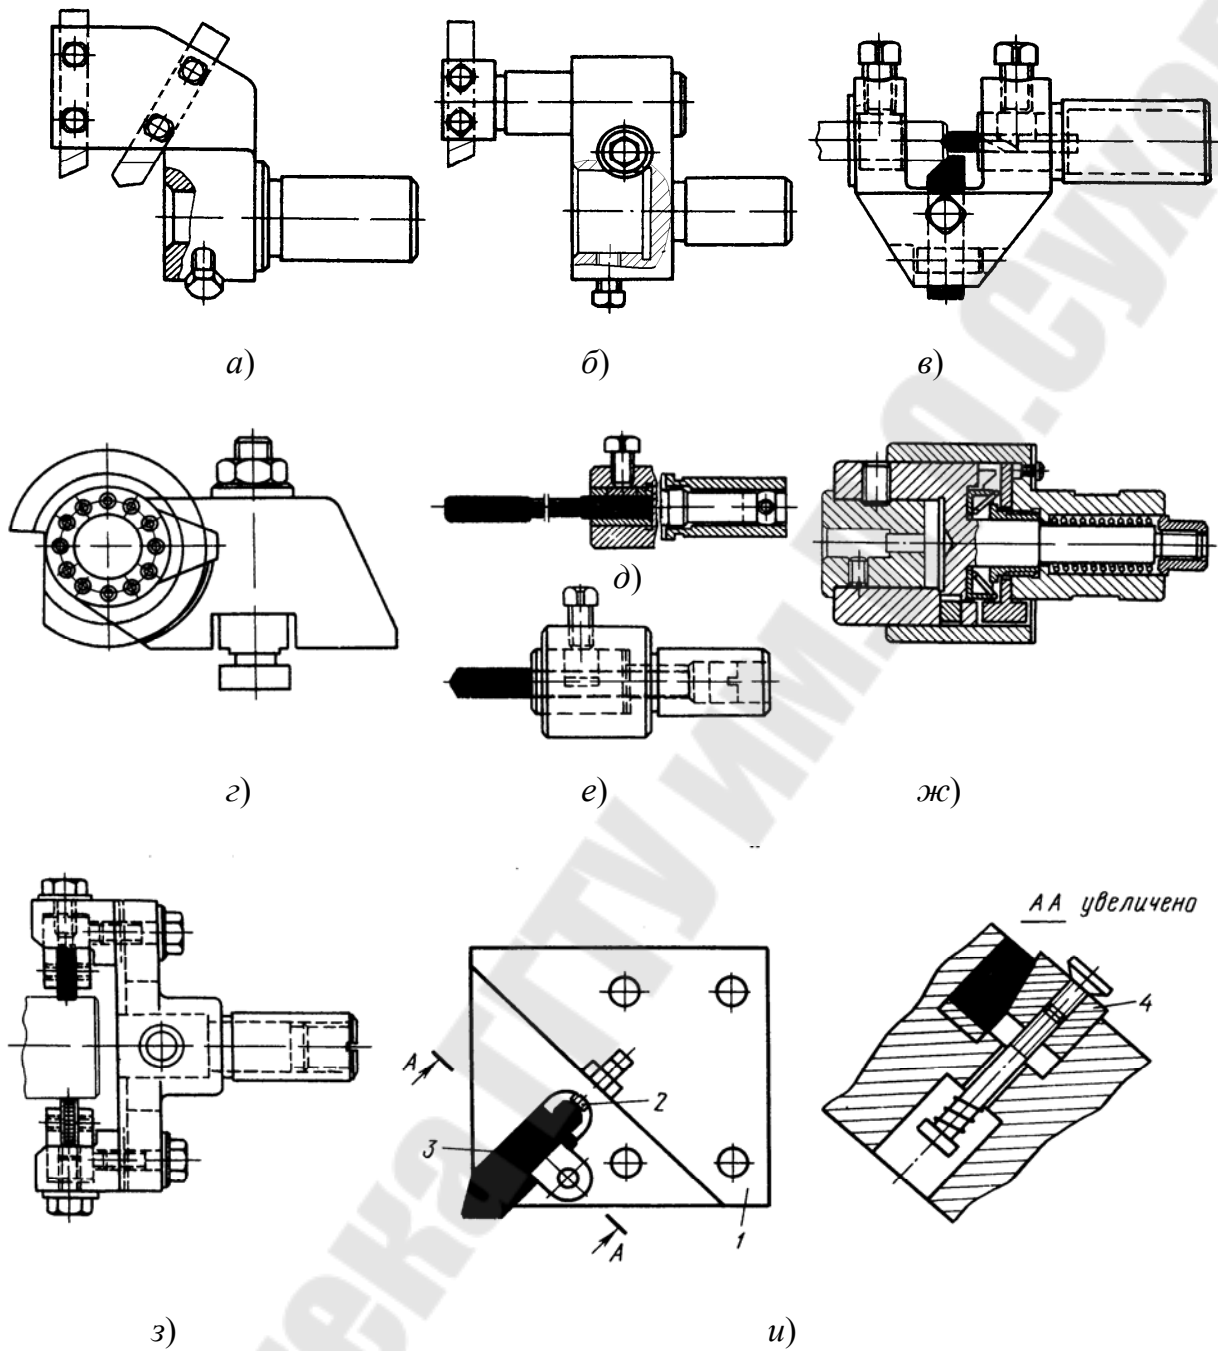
Эскизы державок для установки и закрепления инструментов:
